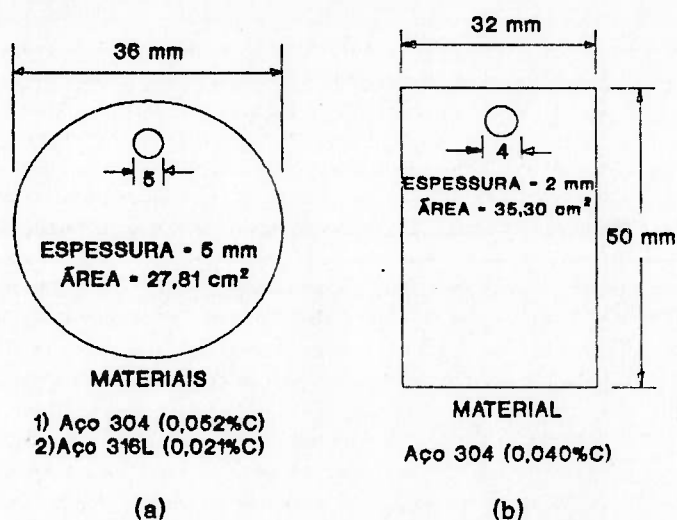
Dimensões dos corpos de prova utilizados para os ensaios; (a) corpos de prova de aços forjados (testes 3.2.1 e 3.2.2); (b) corpos de prova de aços laminados, incluindo os soldados (testes 3.2.3).
